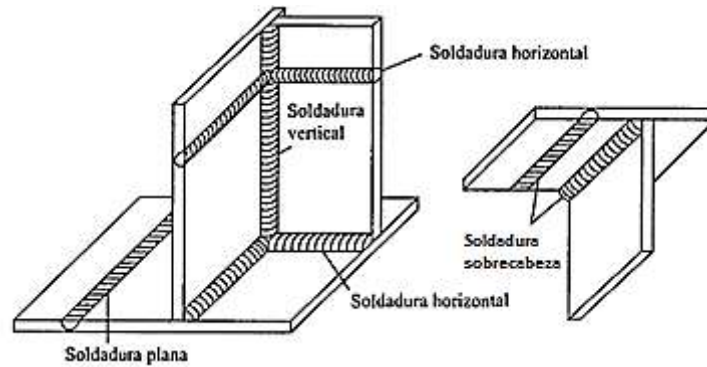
POSICIONES DE SOLDADURA
